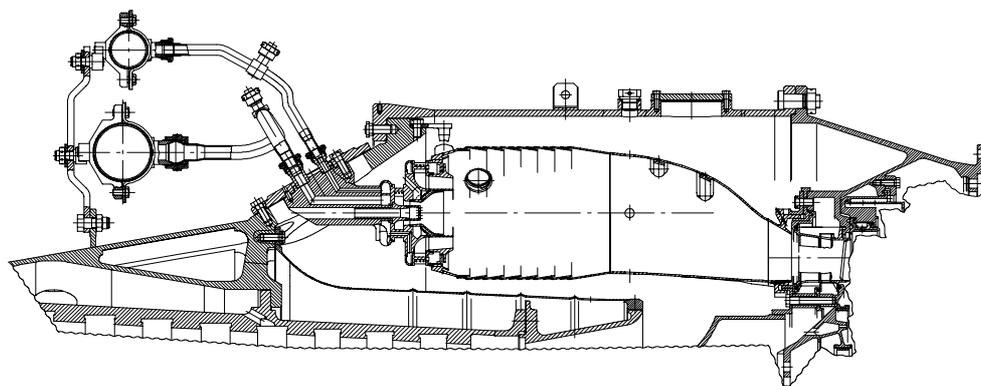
Конструктивная схема камеры сгорания газотурбинного двигателя
